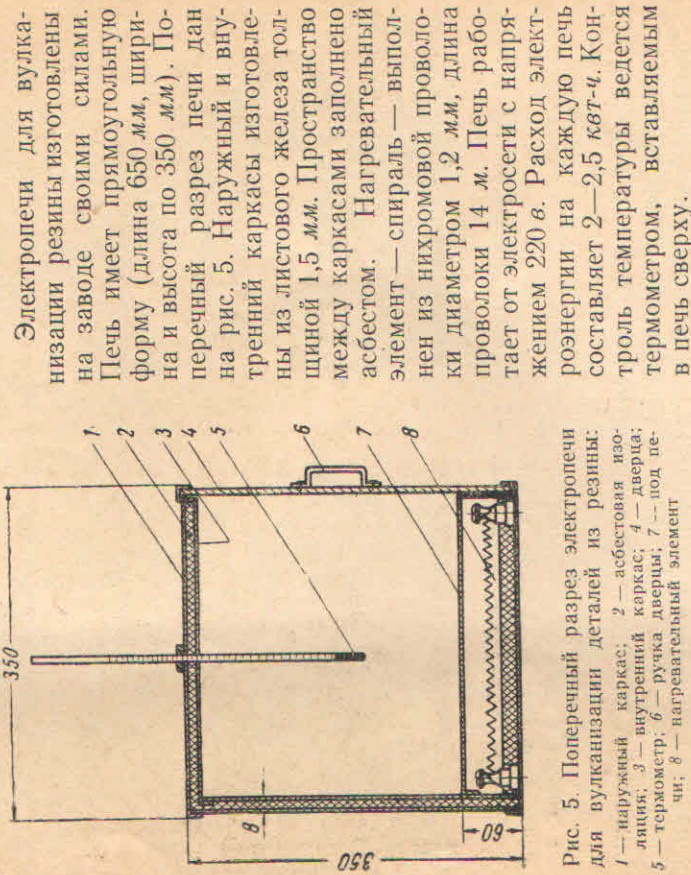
Поперечный разрез электропечи для вулканизации деталей из резины: 1 — наружный каркас; 2 — асбестовая изоляция; 3 — внутренний каркас; 4 — дверь; 5 — термометр; 6 — ручка двери; 7 — под печи; 8 — нагревательный элемент
